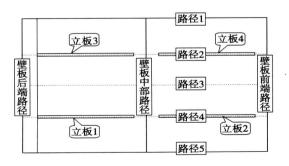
油箱焊接顺序示意图 Fig 4 Welding sequence of oil box
